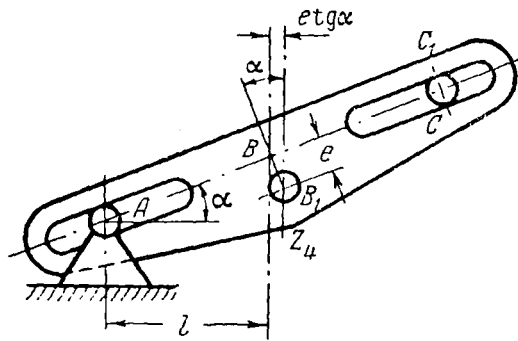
Неточное изготовление правого паза рычага AC.
